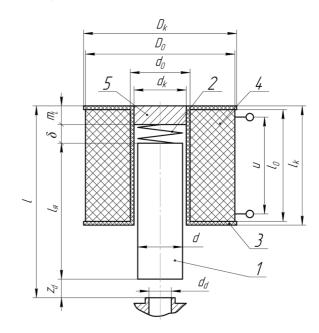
Схема электромагнитного дозатора газа: I – клапан-сердечник перепуска газа; 2 – предварительно сжатая пружина; 3 – корпус катушки; 4 – обмотка катушки; 5 – упор;  $D_{\kappa}$  и  $d_{\kappa}$  - наружный и внутренний диаметры электромагнитной катушки;  $I_{\kappa}$  - длина корпуса катушки
